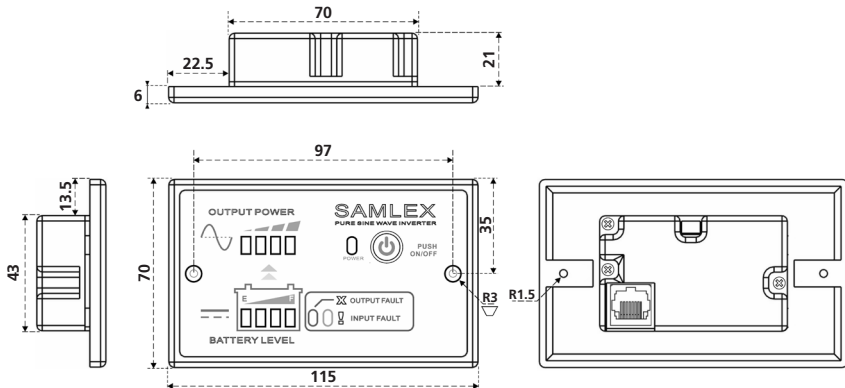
Dimensiones generales y orificios de montaje Control remoto.
